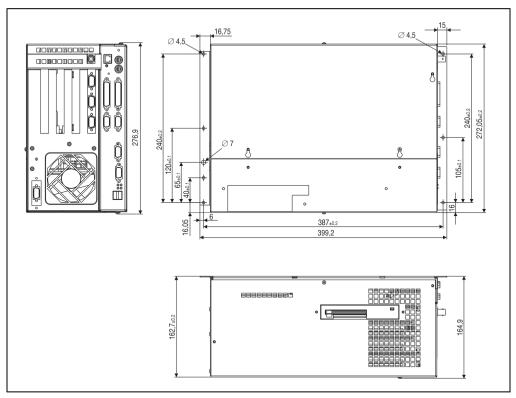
Dimensions IPC5600 / IPC5600C (4 emplacements)
